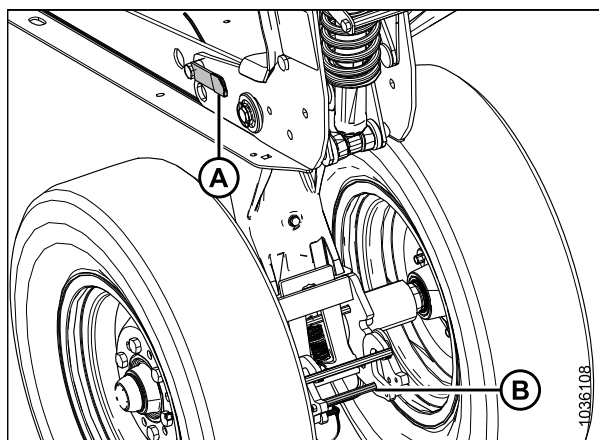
Левые транспортные колеса — шарнир освобожден
